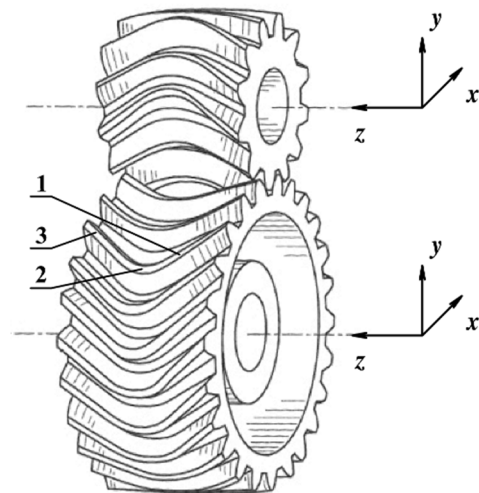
Цилиндрическая эвольвентная передача с арочно-винтовыми зубьями: 1,3 – косозубые участки; 2 – арочный участок зуба
